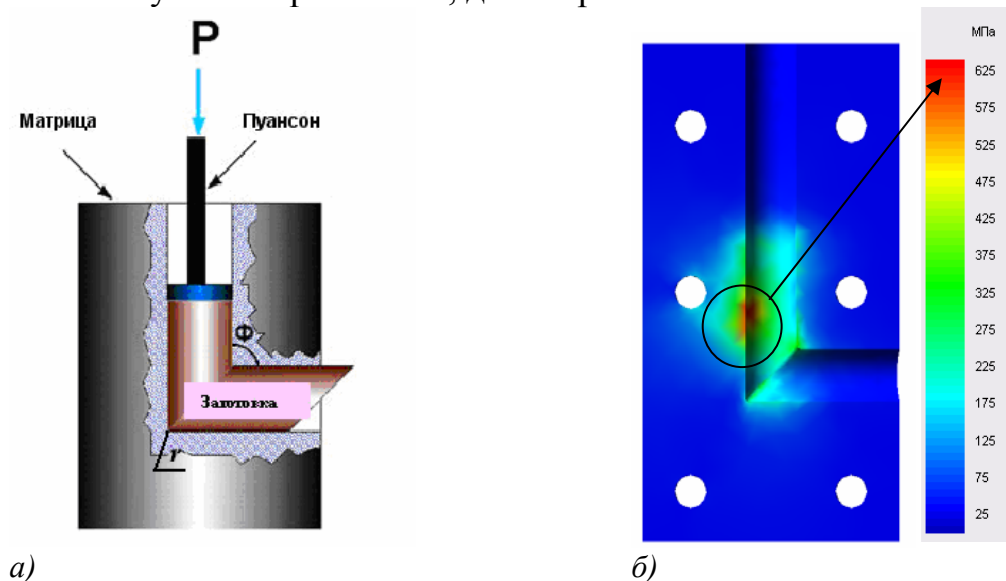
Схема РКУП (а), картина распределения эквивалентных напряжений в сечении оснастки (б)
